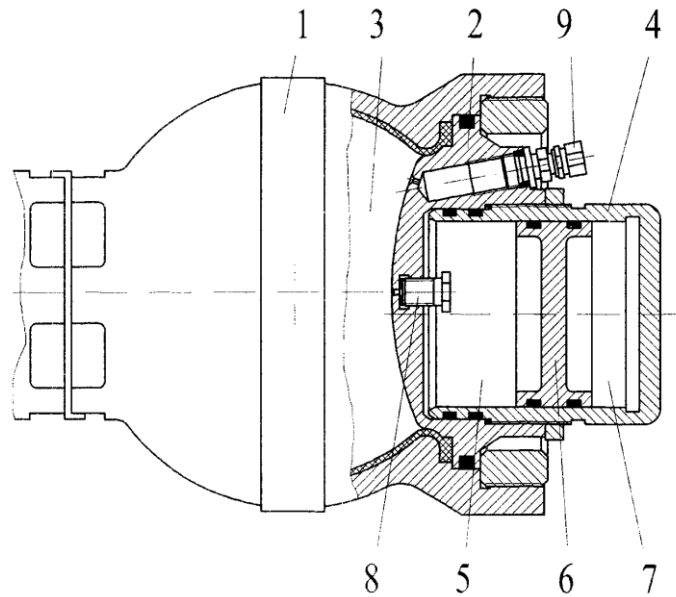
Рессора с гидропневматическим цилиндром компенсации:
